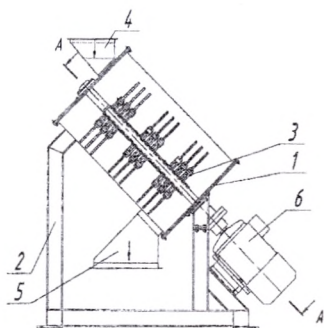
Схема и общий вид молотковой дробилки с наклонным корпусом
